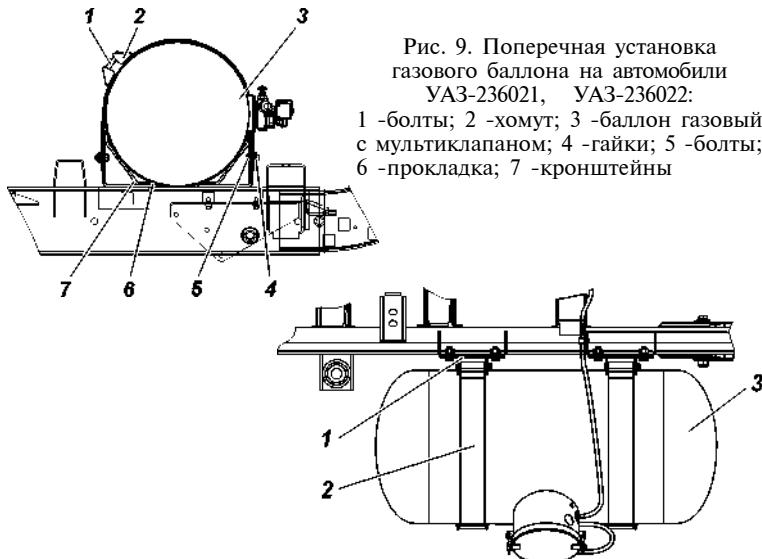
Поперечная установка газового баллона на автомобили УАЗ-236021, УАЗ-236022:
